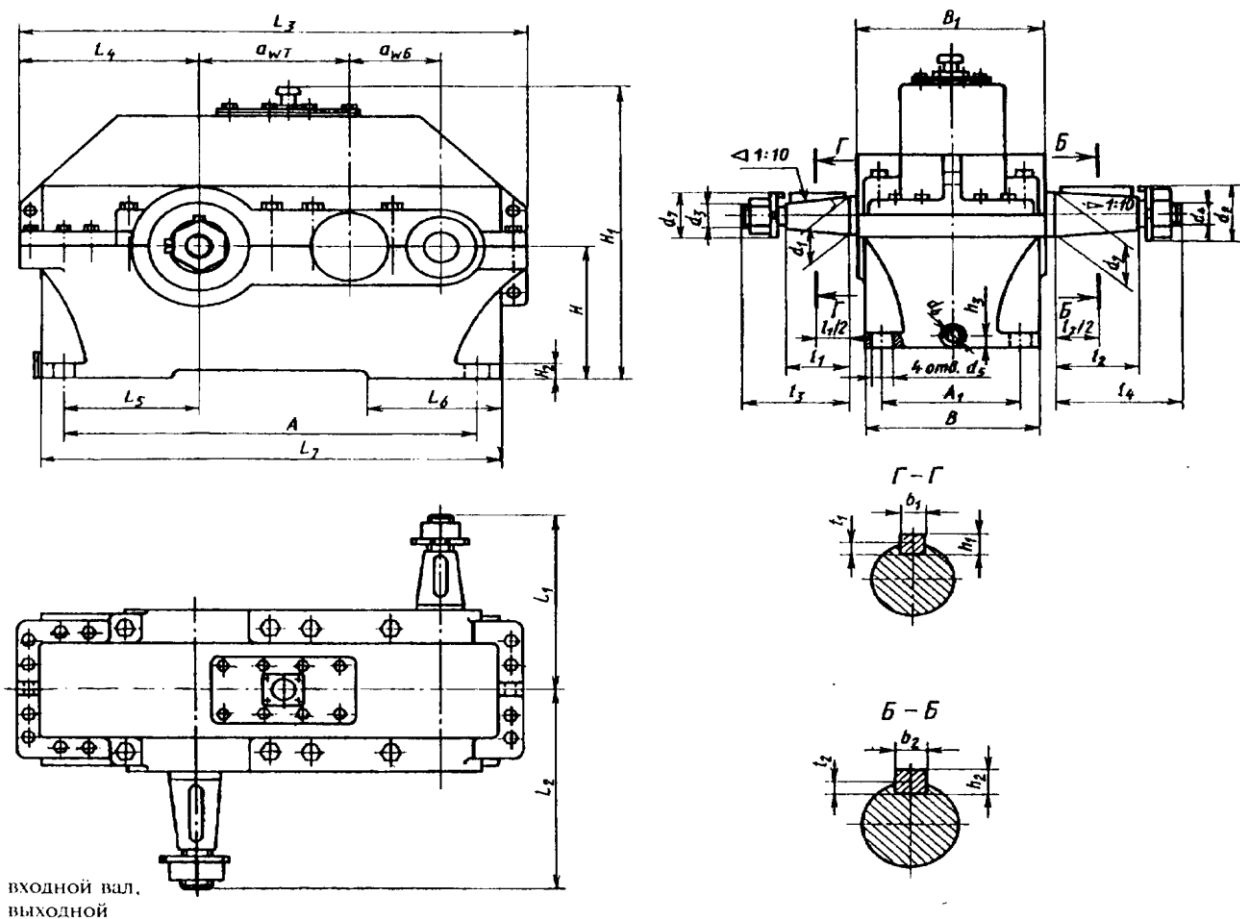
Цилиндрический двухступенчатый редуктор Ц2У-125
